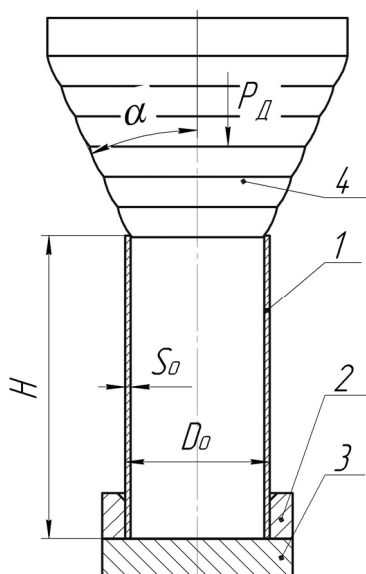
Схема процесу відкритої роздачі трубчастої заготовки
